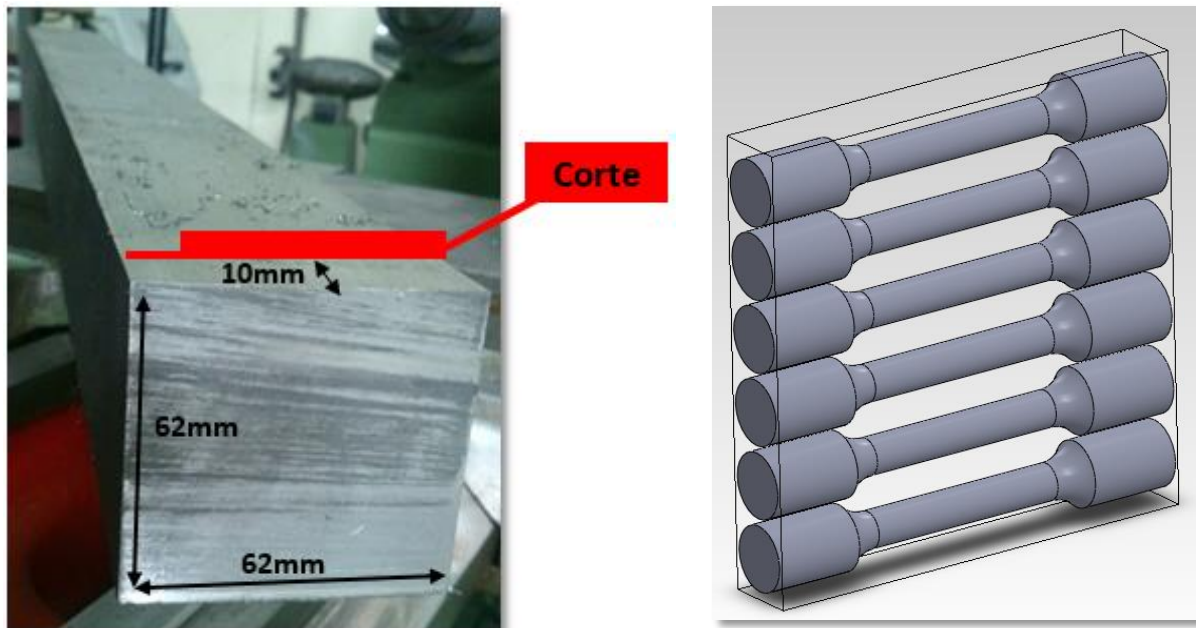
Despiece del cupón de partida (izquierda) y mecanizado de las probetas de tracción.
